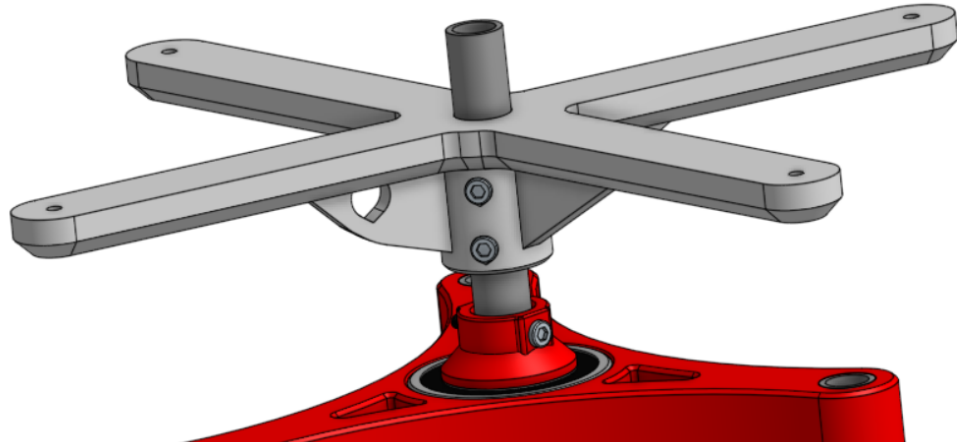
Vista isométrica 1 del ensamblaje del soporte superior con el eje principal en Onshape [fuente: elaboración propia]
